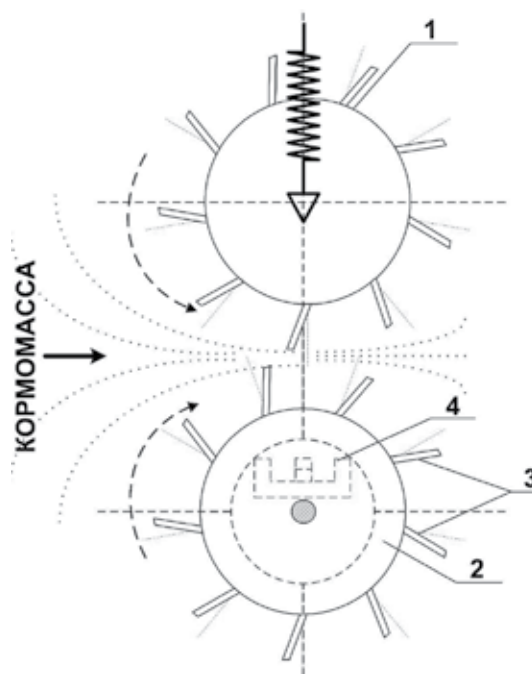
Расположение формующих валцов: 1 – верхний; 2 – нижний; 3 – лопатки; 4 – металлодетектор
